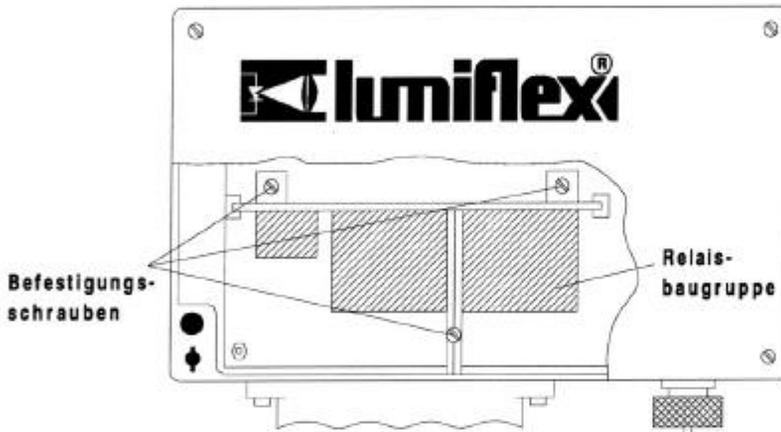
Zum Ausbau der Relaisbaugruppe sind die 3 Befestigungsschrauben zu lösen
